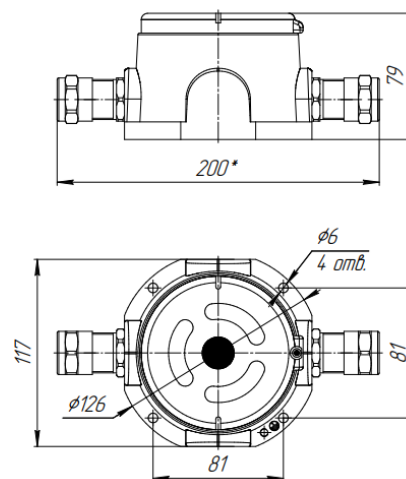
Габаритные и присоединительные размеры, корпус из алюминиевого сплава (А).
